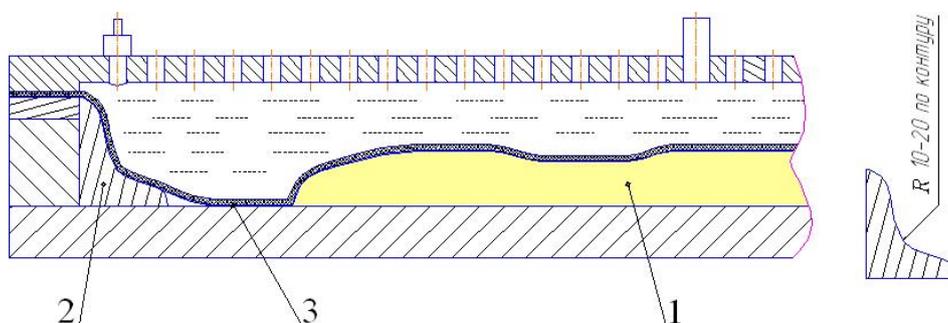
Вариант универсальной штамповой оснастки для пресса ПЭГ-ХАИ-500: 1 – индивидуальный формообразующий блок; 2 – универсальный (вспомогательный) блок-вставка; 3 – заготовка из стального листа
